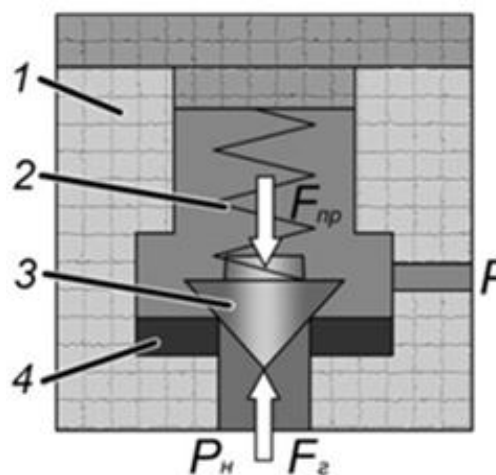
Предохранительный клапан седельного типа: 1 - корпус, 2 - пружина, 3 - запорно-регулирующий элемент, 4 - седло
